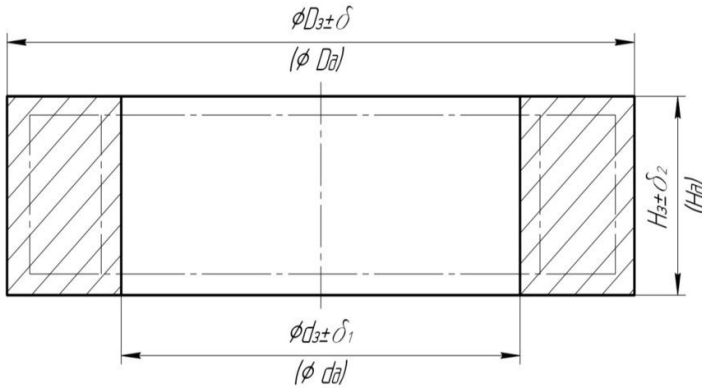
Креслення кованої деталі «Кільце»
